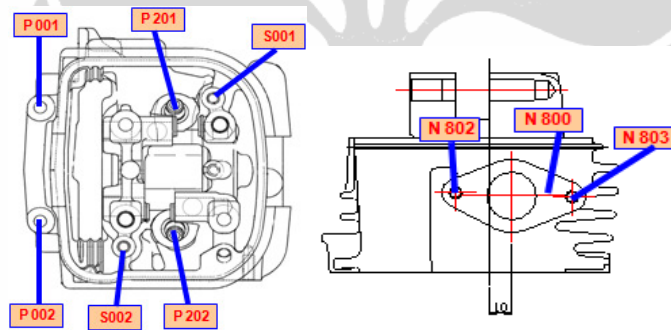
Proses OP 30 *Cylinder Head Machining
